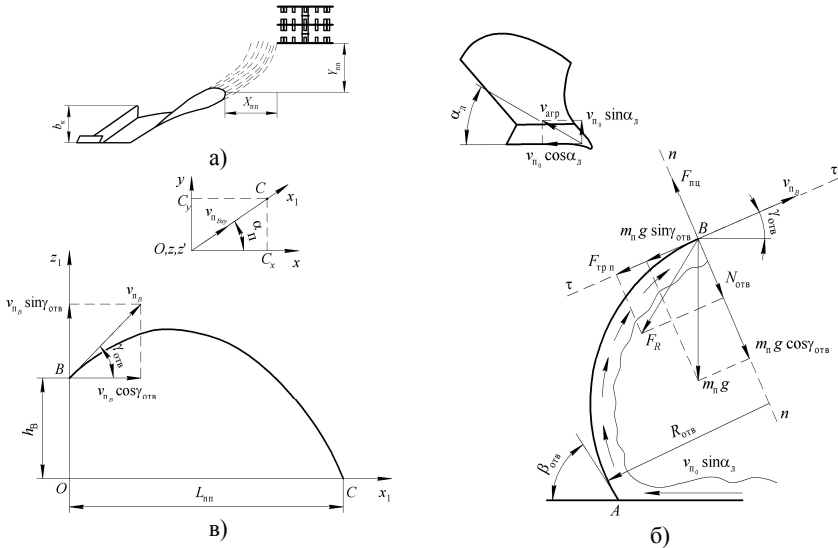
Схема к обоснованию параметров установки катковой приставки относительно корпуса плуга: а – параметры установки приставки (вид сверху); б – схема движения почвенного пласта по поверхности отвала; в – схема полета частицы почвы после схода с отвала
